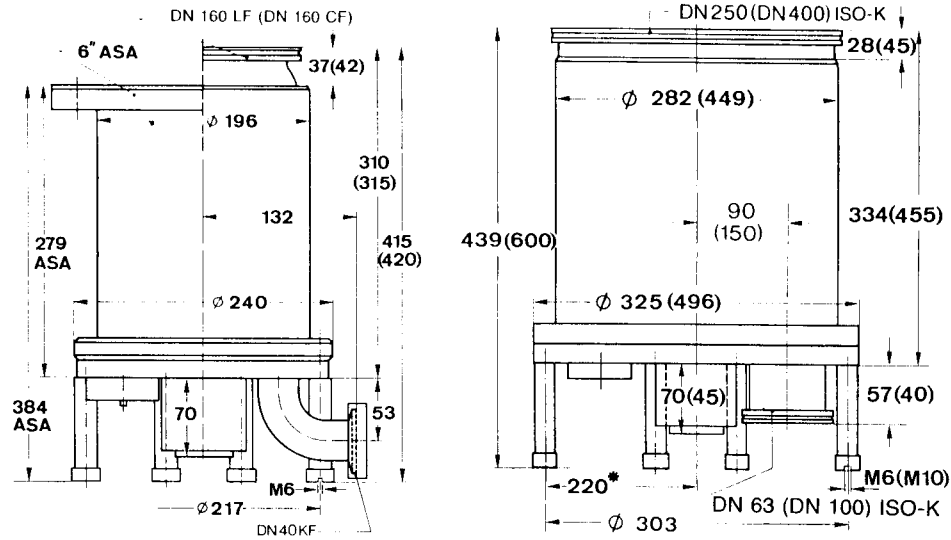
Maßzeichnungen der TURBOVACs; von links 450, 1500 und (3500)
